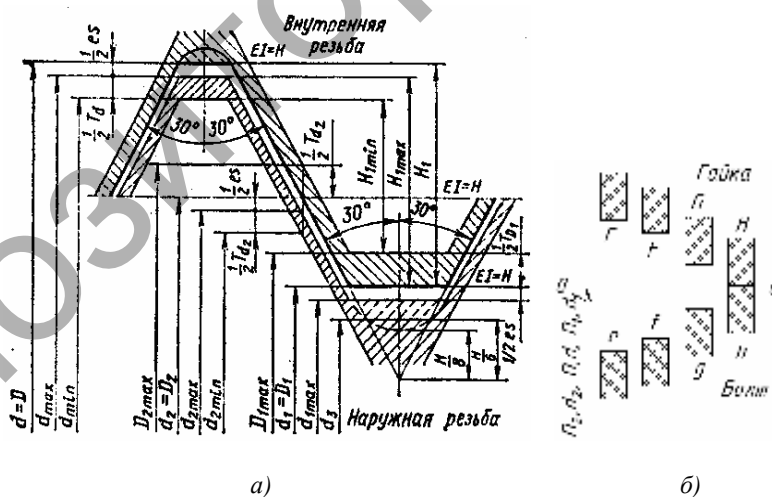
Номинальный профиль метрической резьбы с зазором
